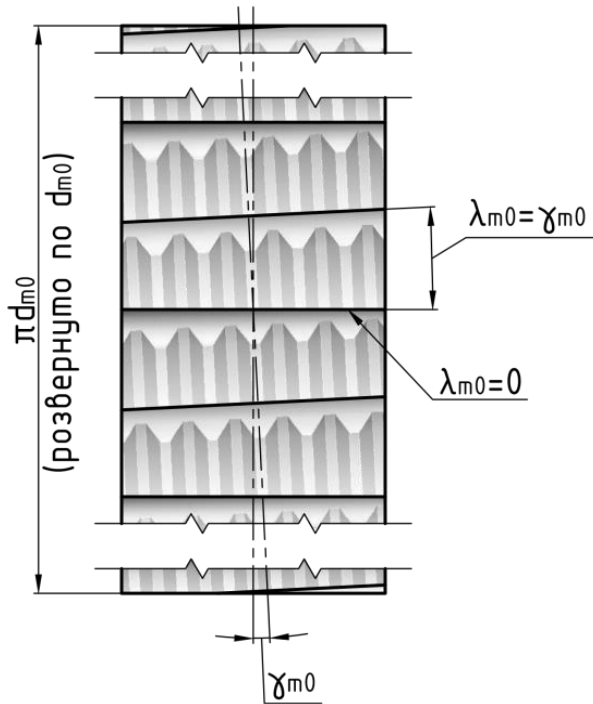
Принципова схема черв'ячної зуборізної фрези з чергуванням суміжних прямих і гвинтових стружкових канавок
